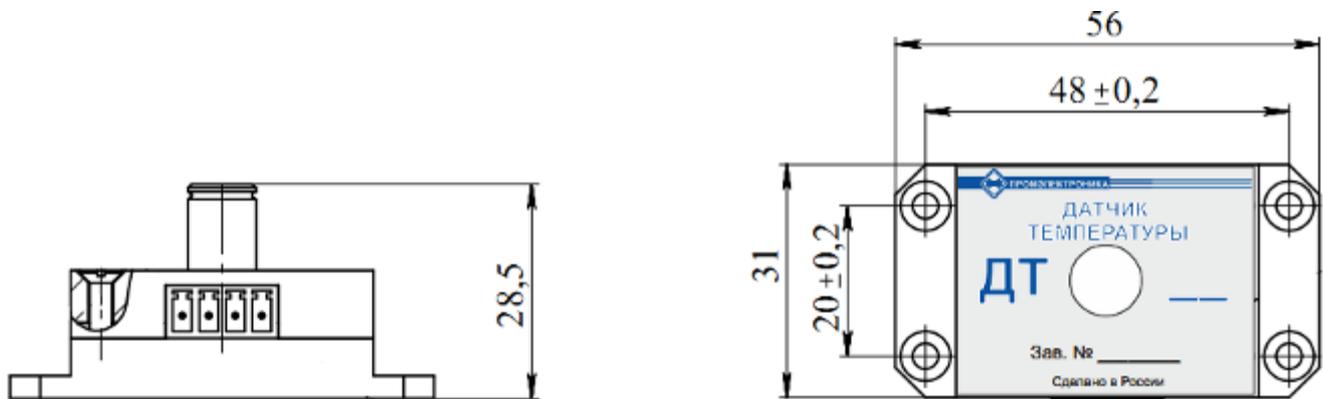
Габаритные и присоединительные размеры ДТ-01
